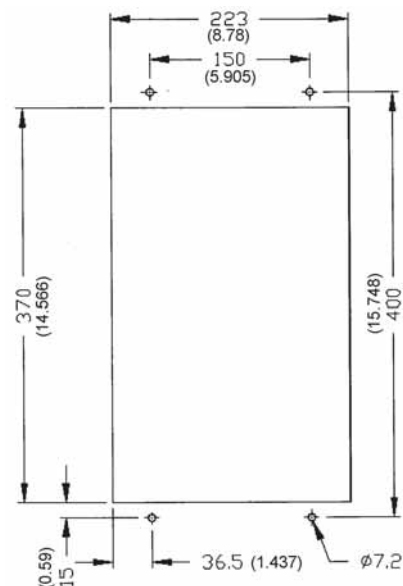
Dimensões do Rasgo para Montagem em Duto
